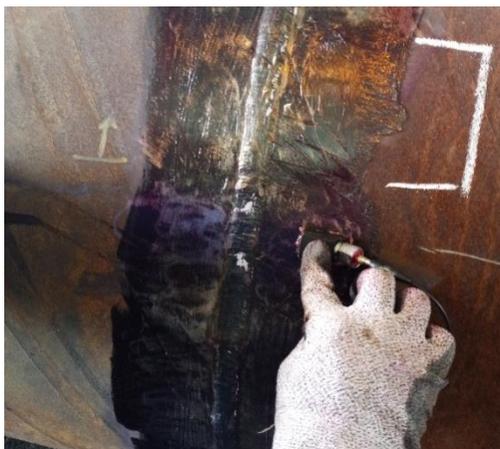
Equipo de ultrasonido para la inspección de soldaduras.
